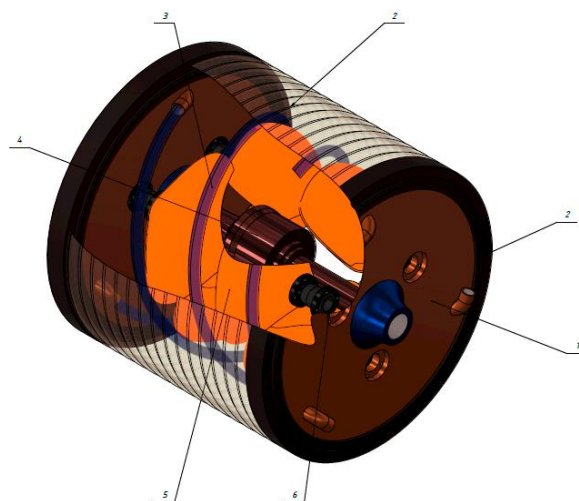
Общий вид позвонка: 1 – крепежная пластина; 2 – крепление для защитного короба; 3 – трубки напорной, всасывающей, а также электрических датчиков и проводов; 4 – шаровый шарнир; 5 – подушки; 6 – гибкие муфты крепления
